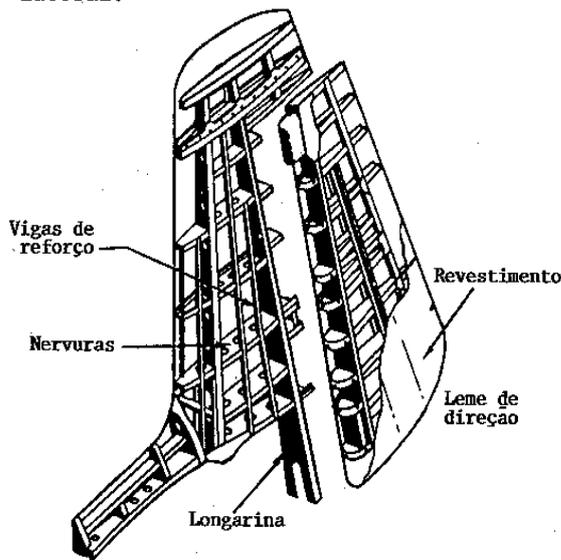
Características de construção do estabilizador vertical e do leme de direção.
